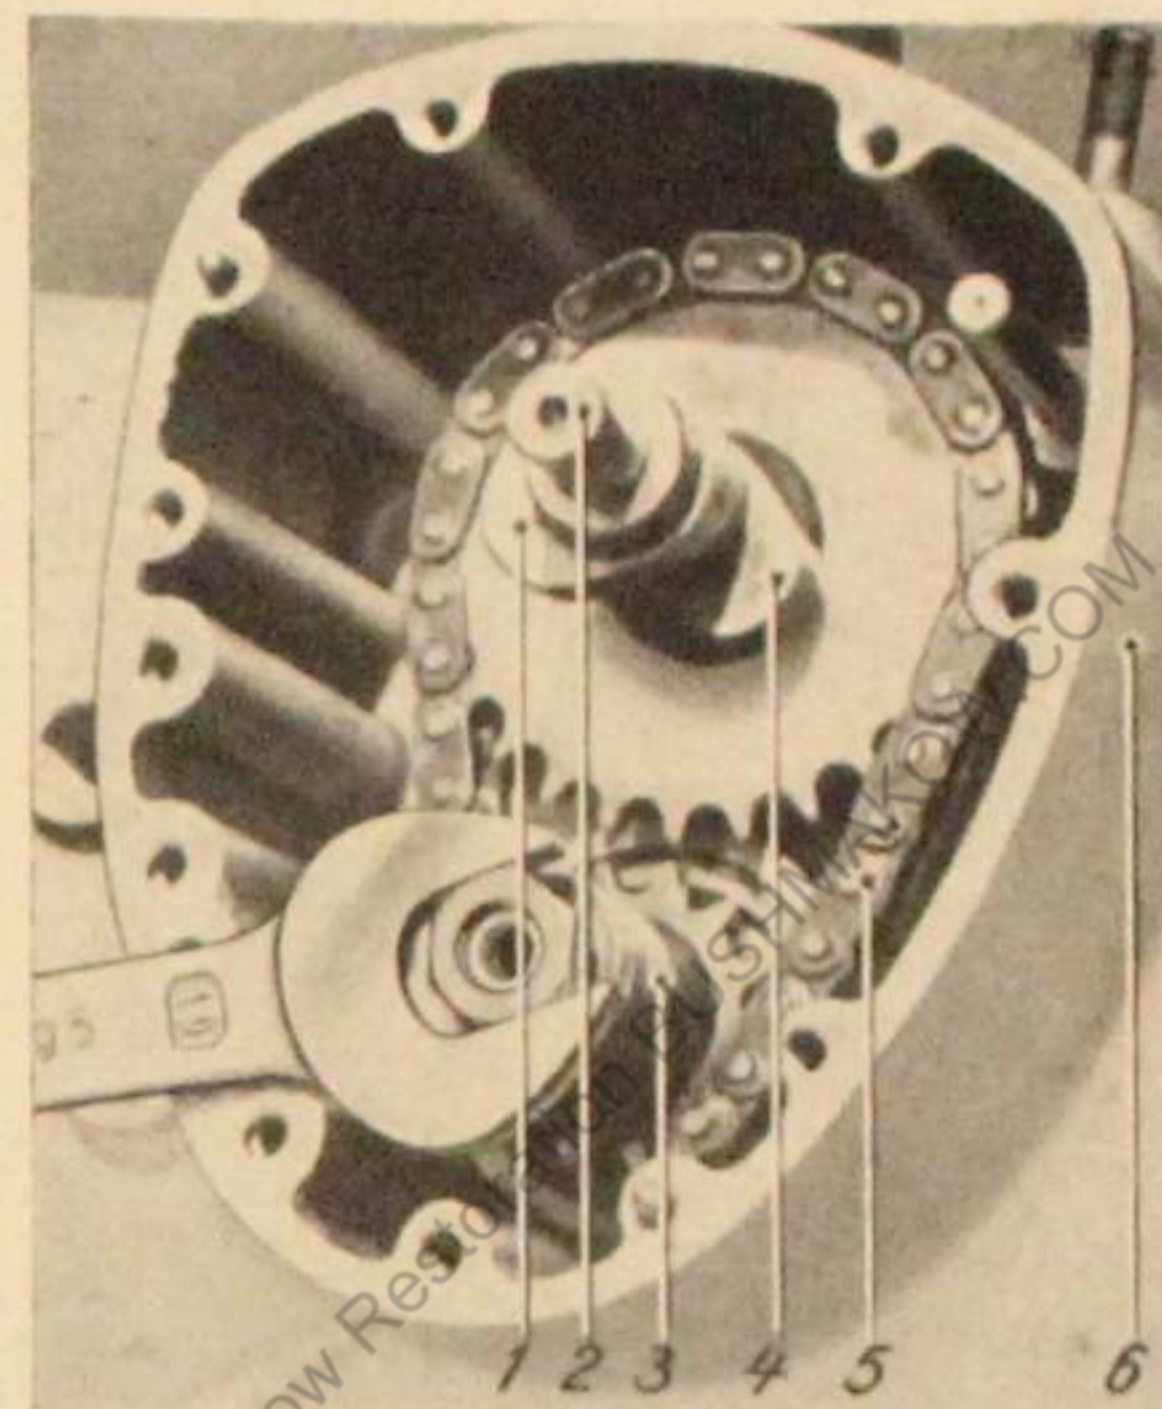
Ansetzen der Abziehvorrichtung zum Kettenrad für Steuerung mit Schnecke
